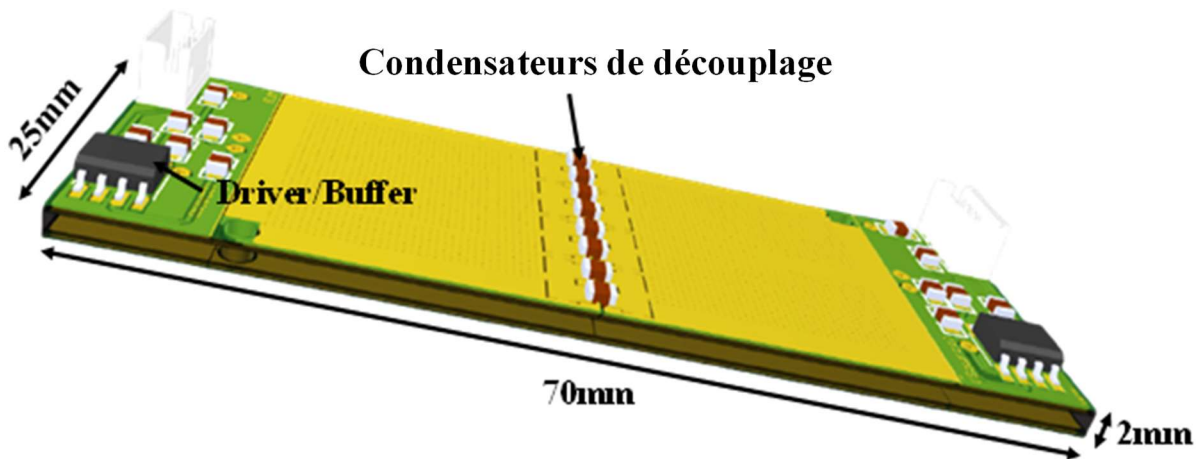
Vue 3D du PCB de puissance de la cellule PM2E
